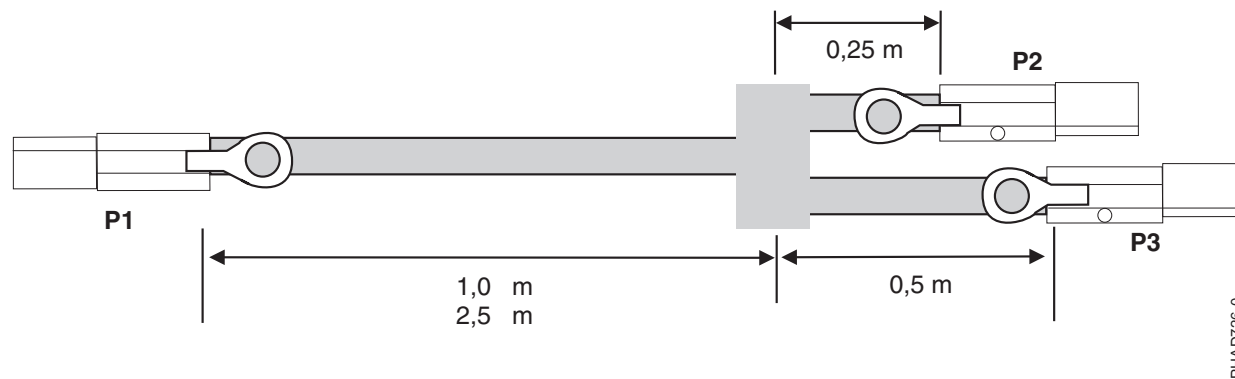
Longitudes de cable de conjunto de cables YI SAS externos
